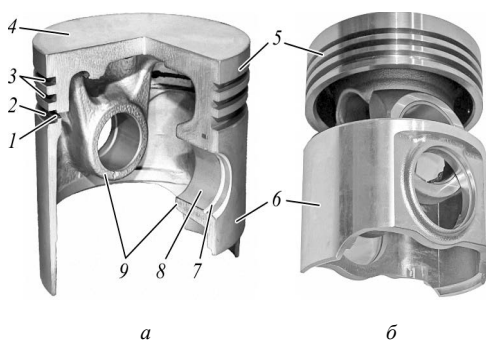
Поршень: а – цельный; б – составной; 1 – отверстия для слива масла; 2 – канавка под маслосъемное кольцо; 3 – канавка под компрессионное кольцо; 4 – днище; 5 – головка; 6 – юбка; 7 – канавка под стопорное кольцо; 8 – отверстие под поршневой палец; 9 – бобышка
